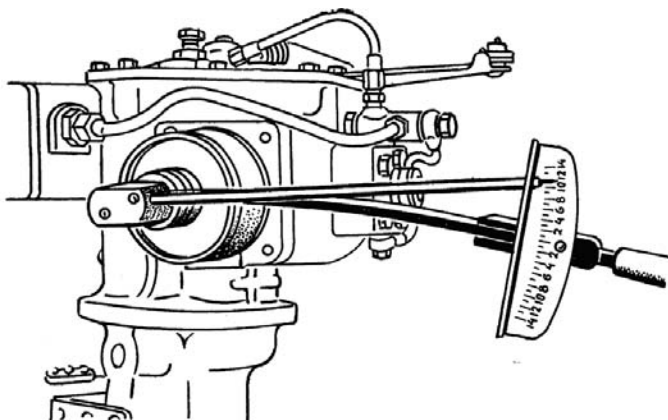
Затяжка гайки крепления поршня гидроусилителя.
